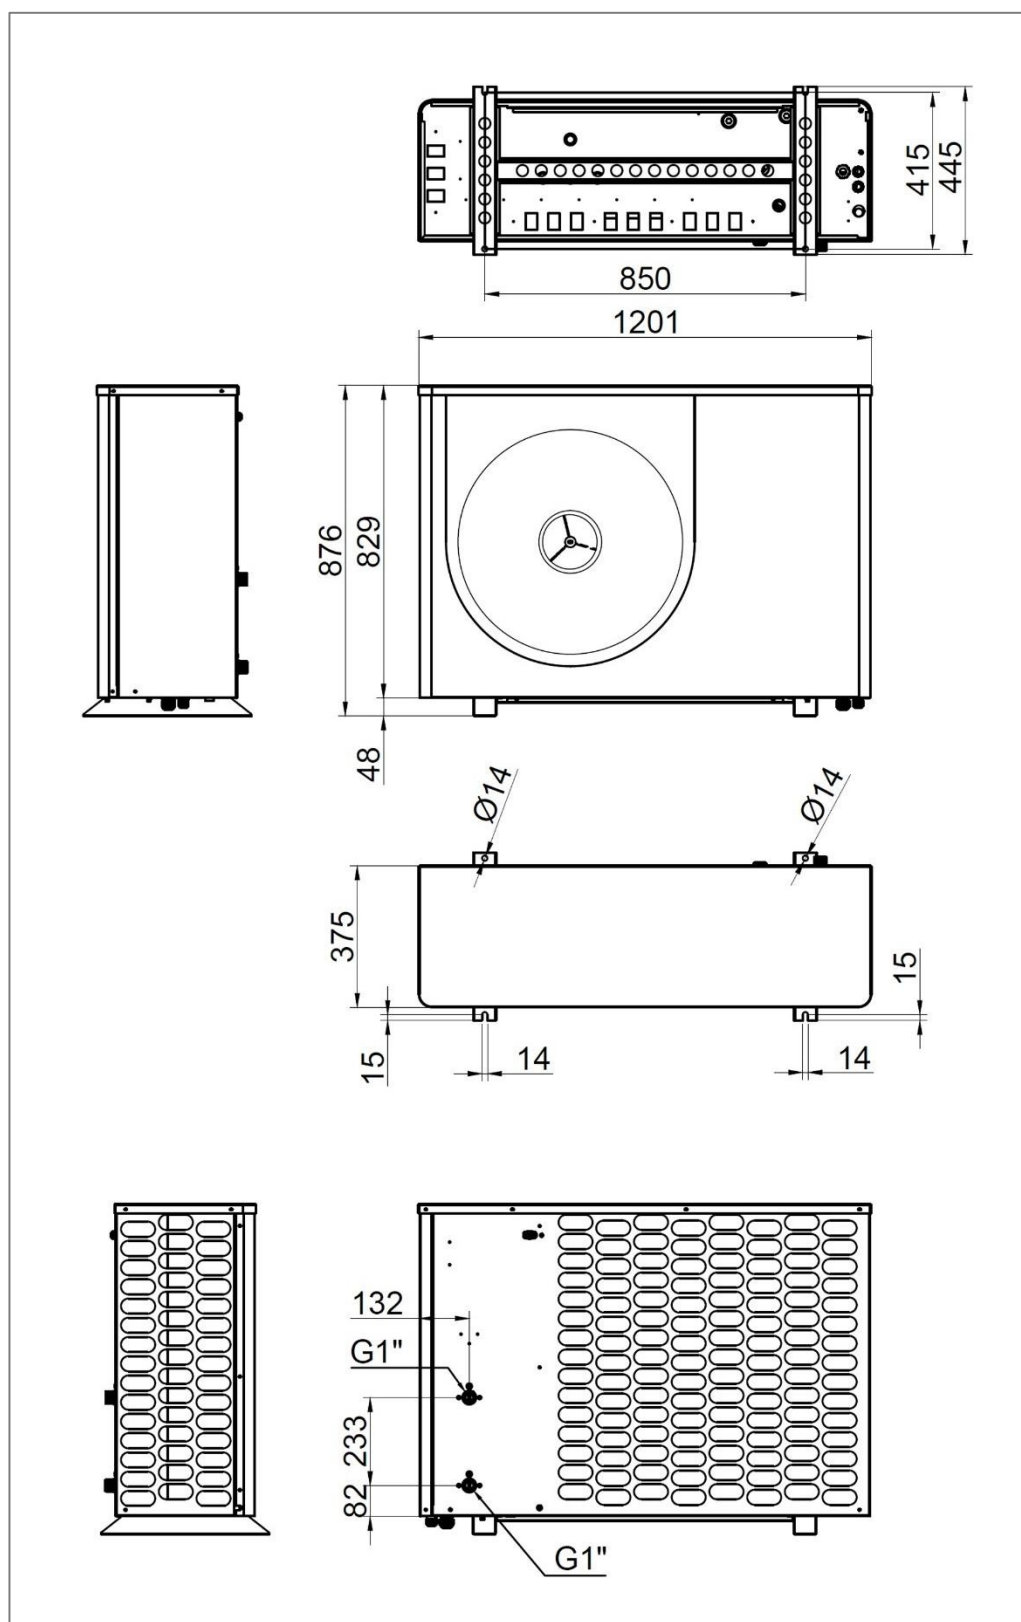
Dimensions de l'unité extérieure MB70008A - Dimensions en mm
